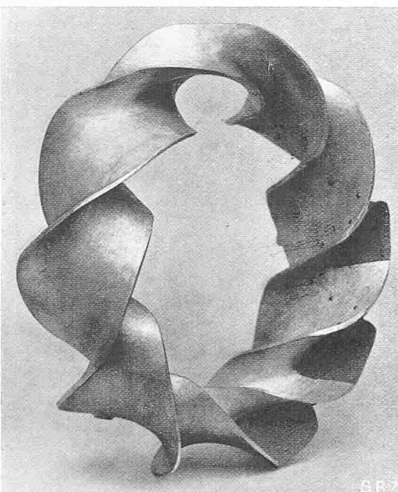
Die aus Aluminium gegossene, dreigängige Verteilungspirale für das Gasgemisch.
